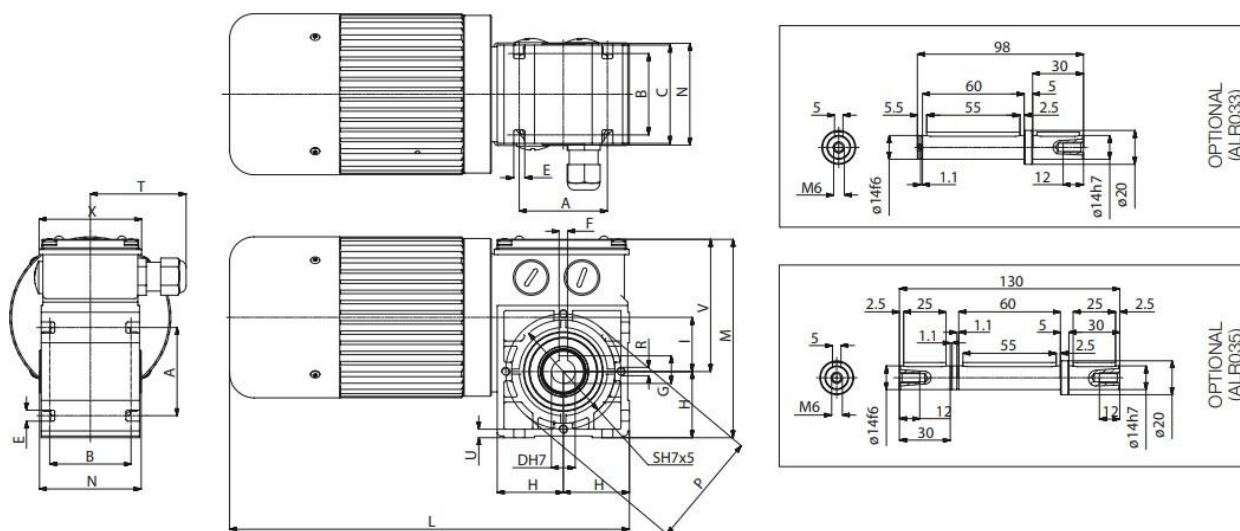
Сервомотор-редуктор PC 165M3 [29, с. 80]
